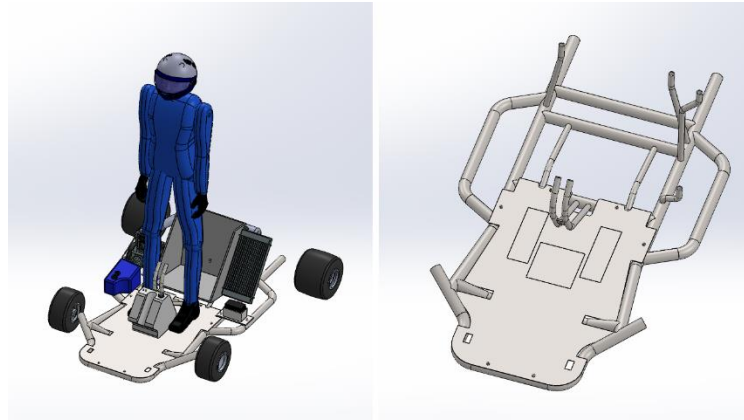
Situación que se simulará y zonas de la plancha donde se aplicarán las fuerzas.
